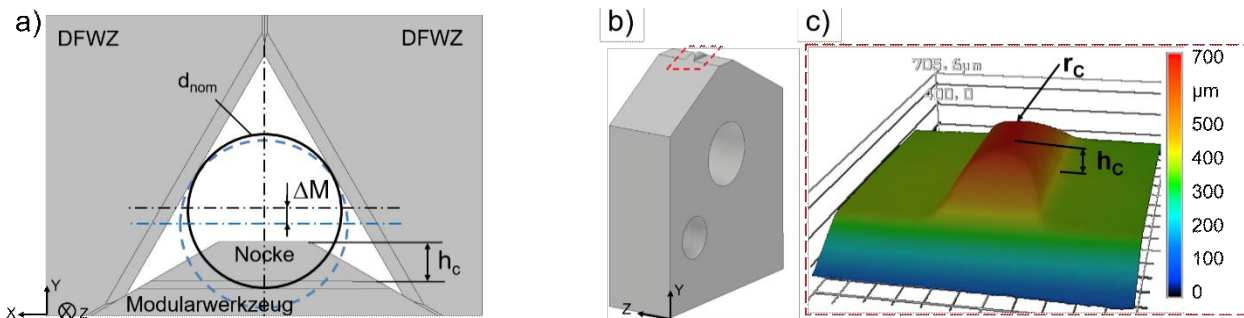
Werkzeugkonzept modularer Werkzeuge a) Bildung eines ungleichseitigen Dreiecks durch zwei Flächen der DFW und eine Fläche des modularen Werkzeuges; b) Werkzeugmodul mit Nocken; c) Messung des Modulnockens, nach [Ish20b].
